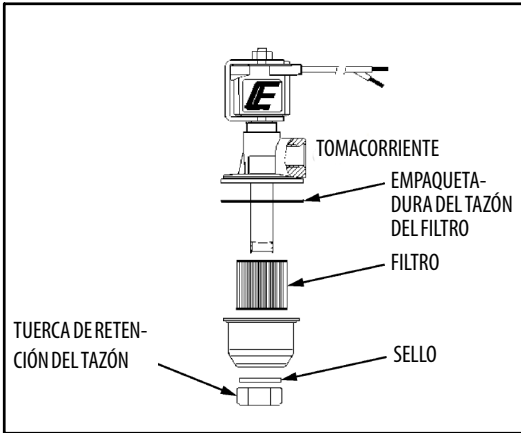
Kubota Conjunto de bloqueo del filtro
